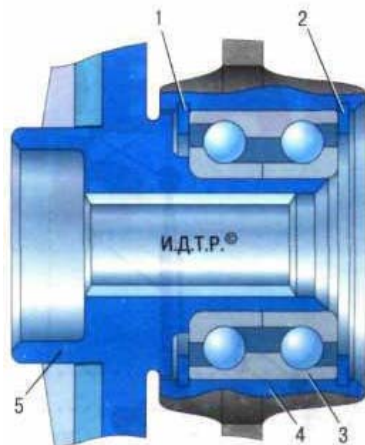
Подшипник передней ступицы: 1,2 - стопорные кольца; 3 - подшипник; 4 - кулак амортизаторной стойки; 5 - ступица
